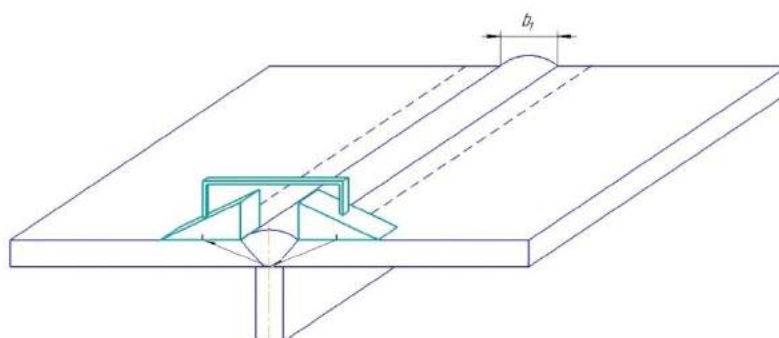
Поперечно-продольная схема сканирования стыковых сварных соединений наклонным ПЭП по совмещенной схеме прямым и однократно отраженным лучами:
